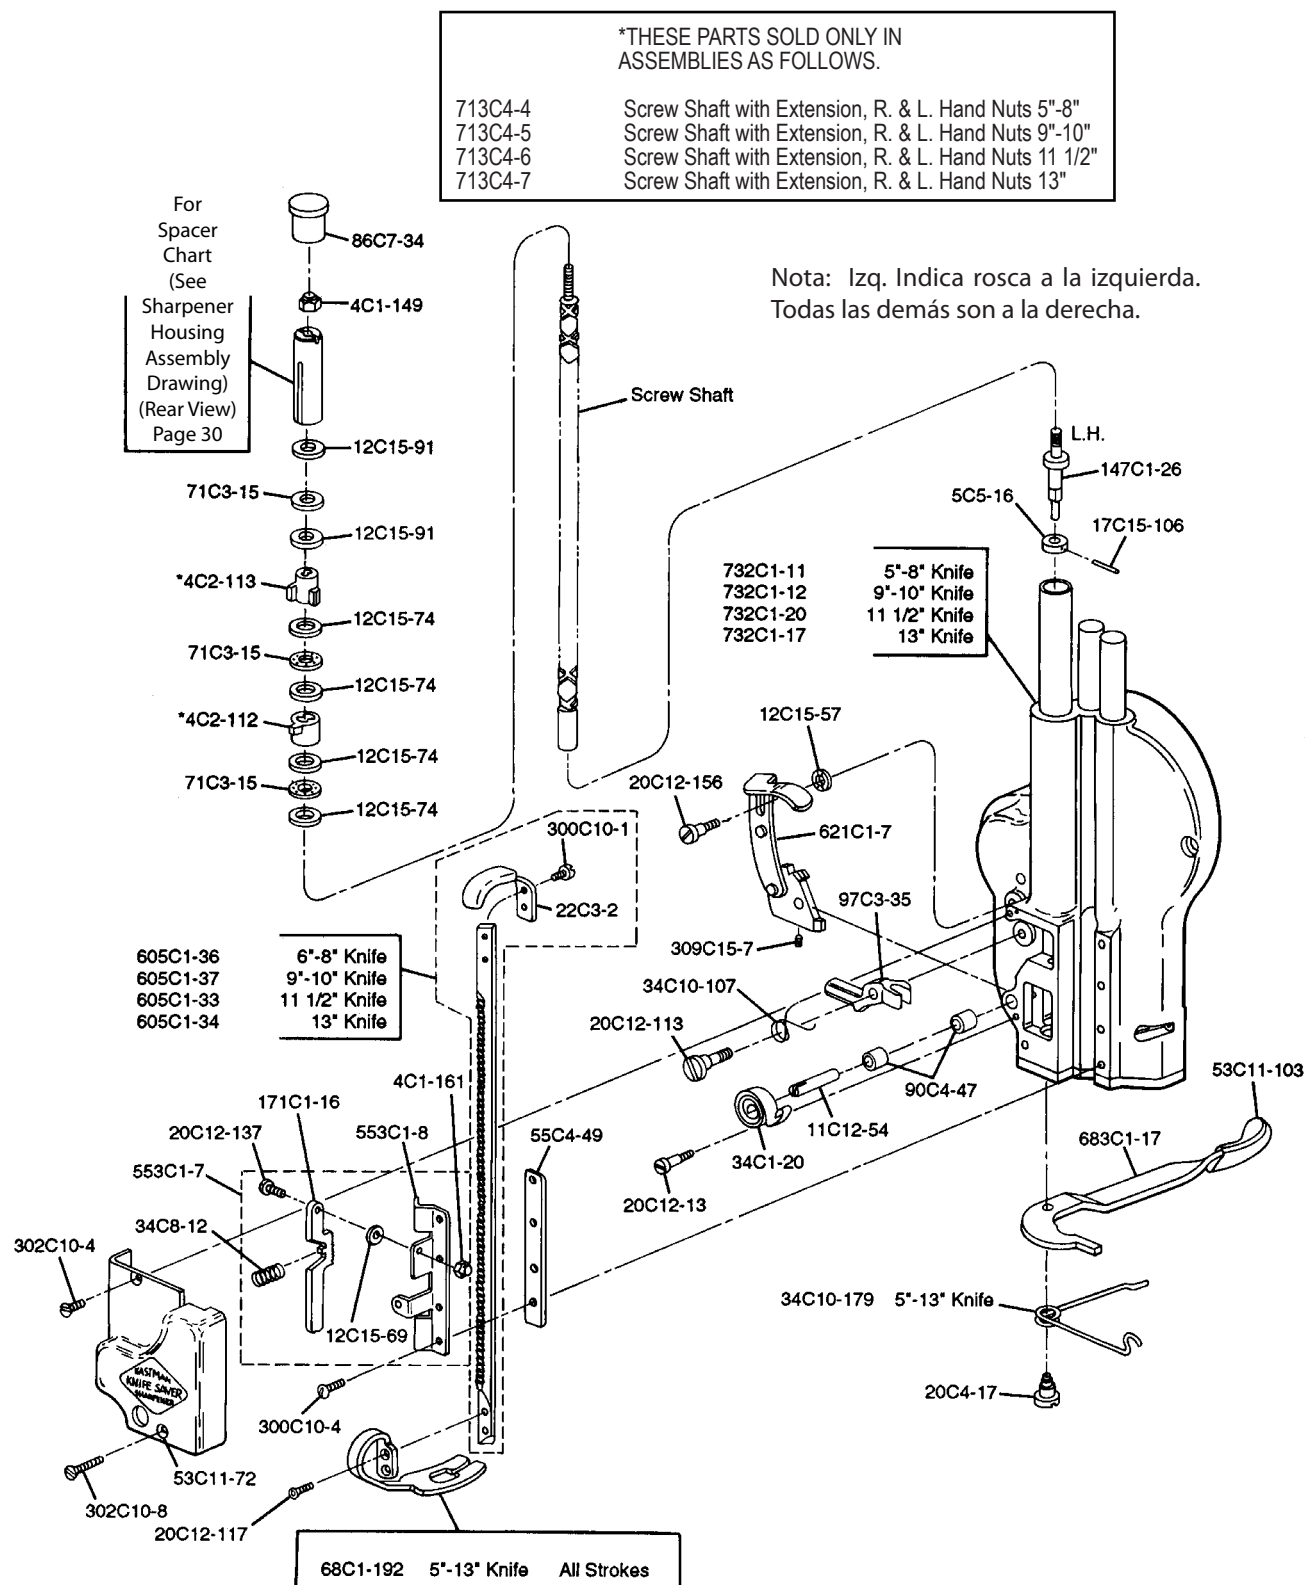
Conjunto de la carcasa del afilador (vista delantera detallada)
